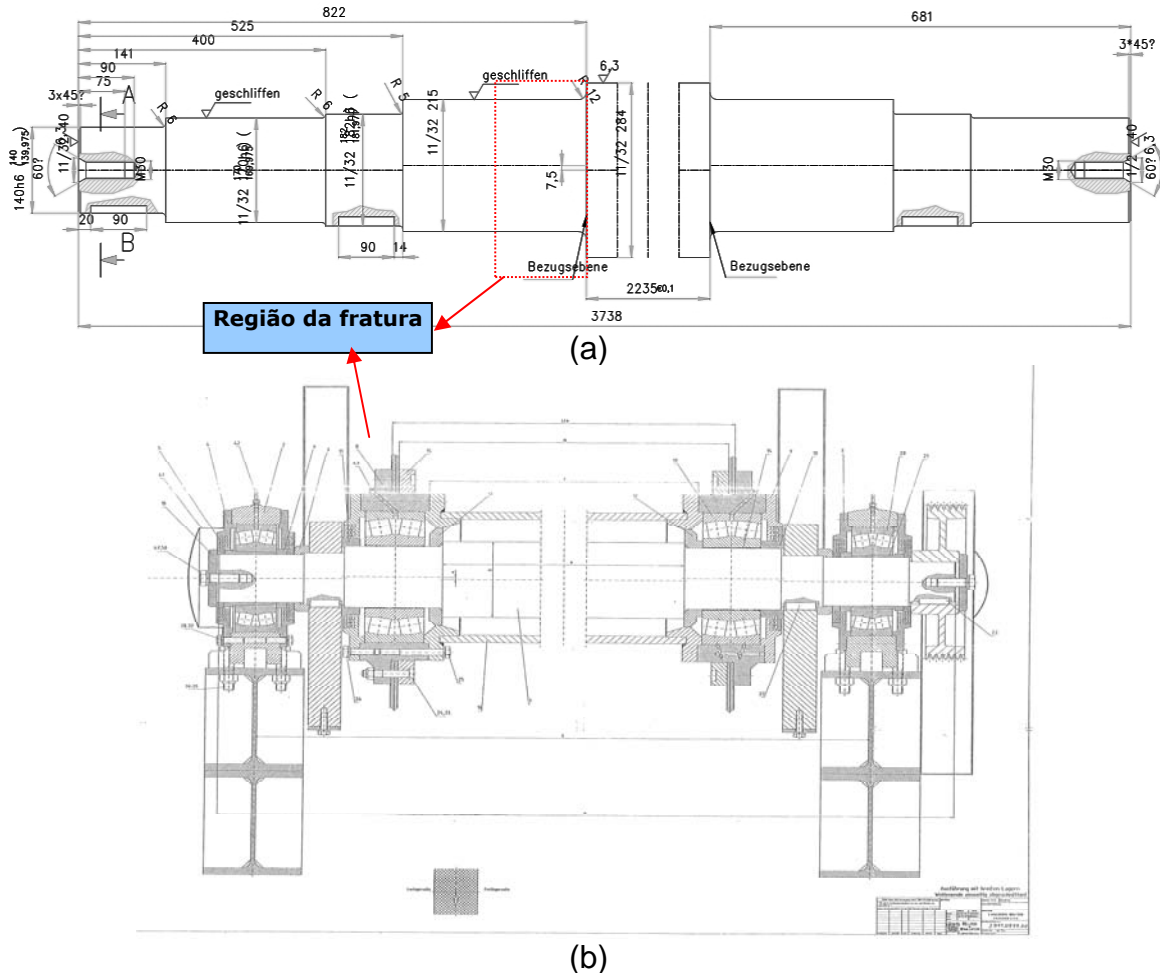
(a) Desenho do eixo excêntrico com detalhe da região da fratura e (b) desenho de montagem dos rolamentos.
